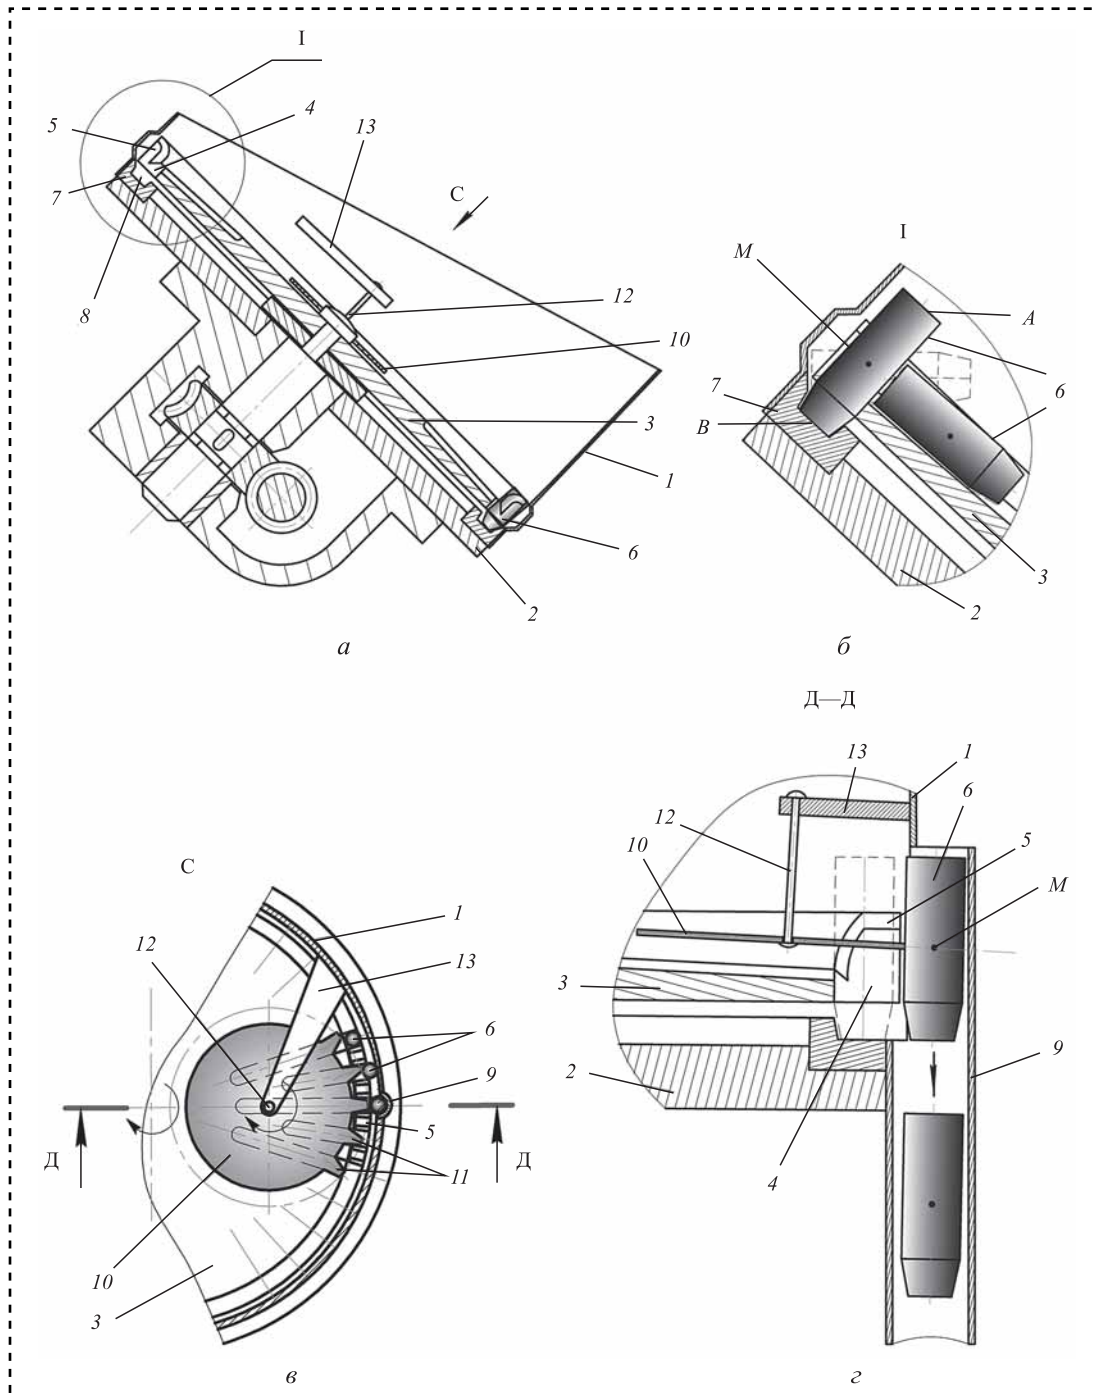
Дискосое зубчатое бункерное загрузочное устройство с выдающей зубчатой звездочкой: *a* — общий вид в разрезе; *б* — положение деталей в верхней части бункера; *в* — вид С на зубчатую звездочку; *г* — разрез Д-Д по оси приемника в зоне выдачи детали
